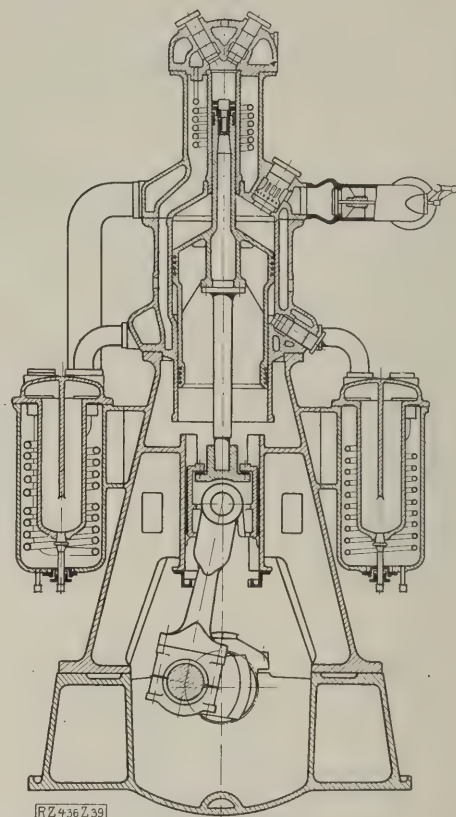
Dreistufiger Luftkompressor für Anlaß- und Einspritzluft der Dieselmachine, Abb. 37.
